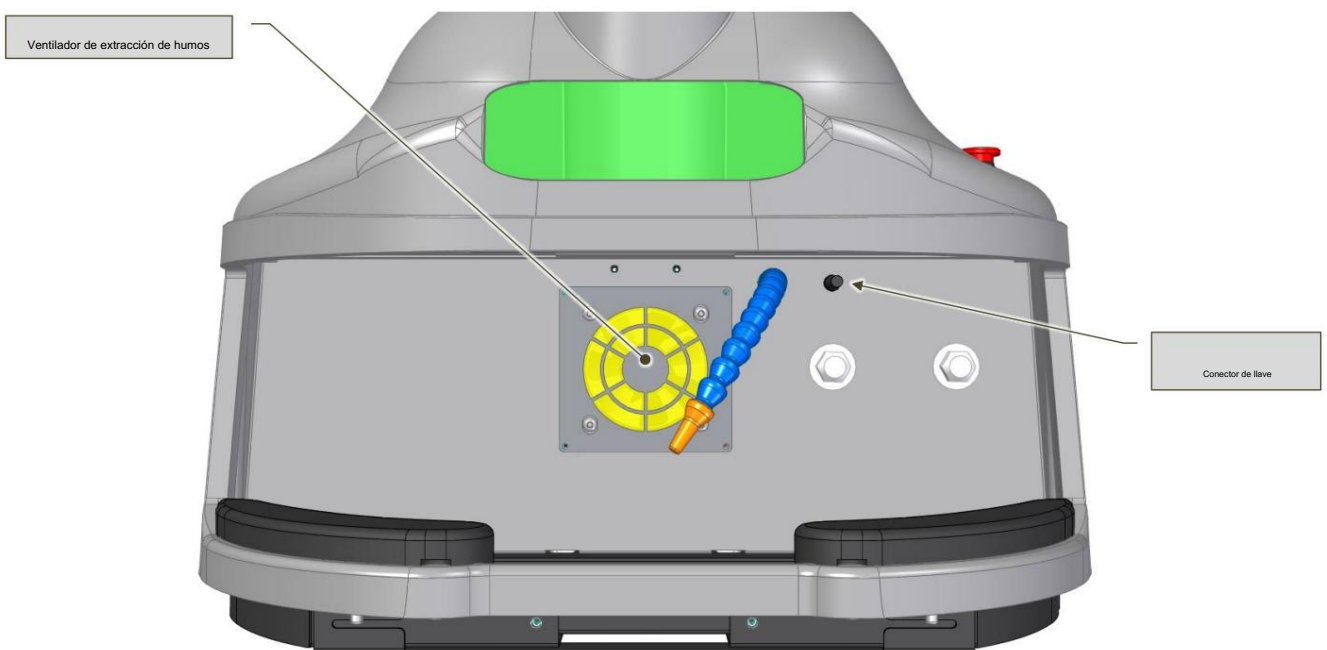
Cámara de soldadura (sin persiana)
